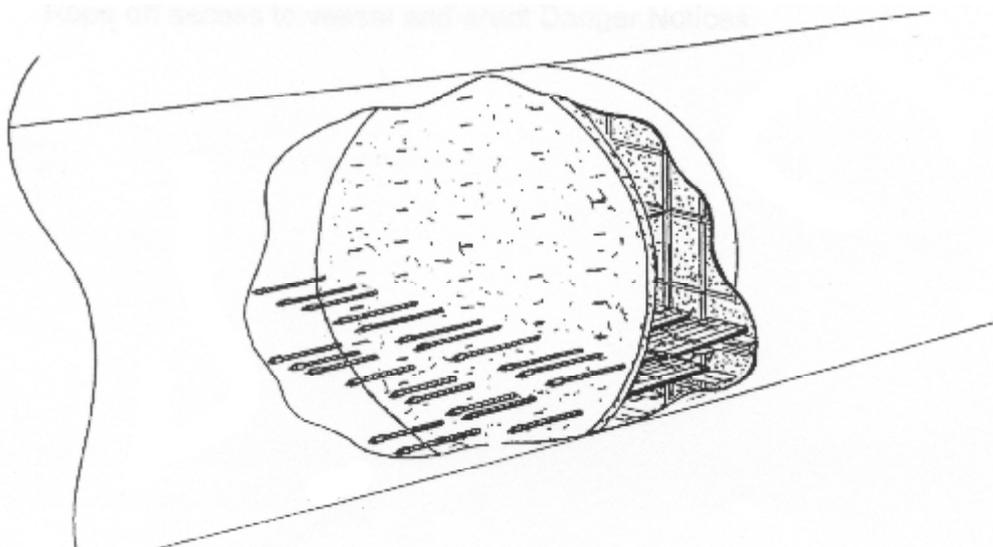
Термообработка замыкающего шва корпуса аппарата большого диаметра
